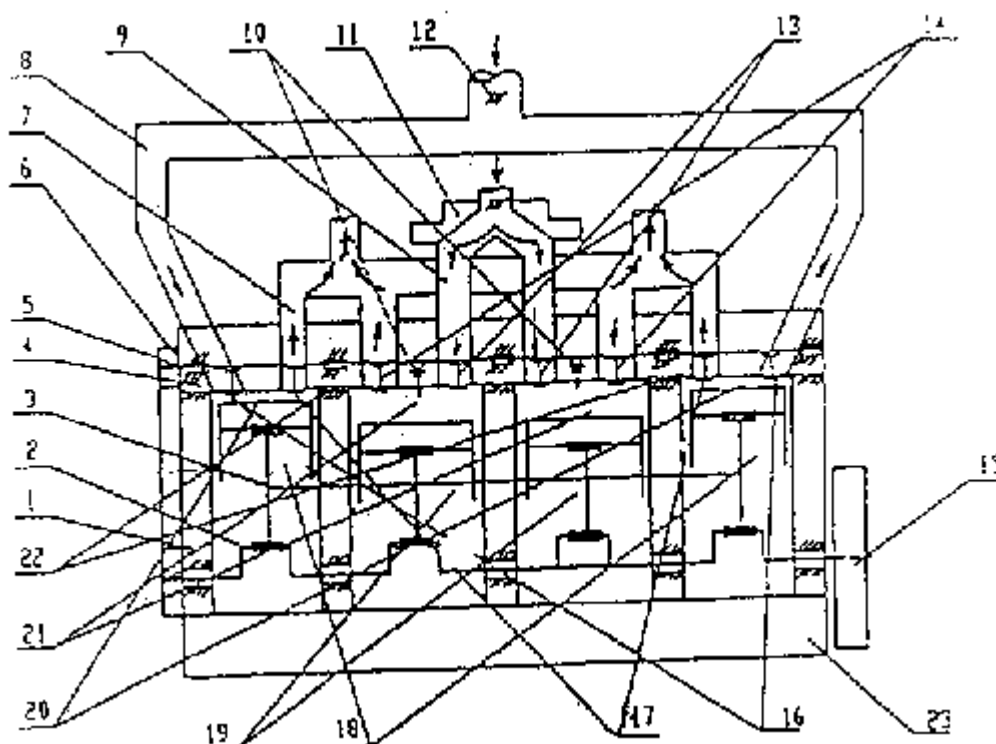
Принципиальная схема ДВС со смежно работающими цилиндрами и искровым зажиганием: 1 – блок цилиндров; 2 – коленчатый вал; 3 – шатуны; 4 – головка блока; 5 – кулачковый вал; 6 – привод; 7, 8, 9 – выпускные и впускные коллекторы; 10 – свечи зажигания; 11 – карбюратор; 12 – воздушная заслонка; 13, 14 – впускные и выпускные клапаны; 15 – маховик; 16, 17 – впускные и выпускные клапаны; 18, 19 – поршни; 20, 21 – камеры сгорания; 22 – канал; 23 – картер
